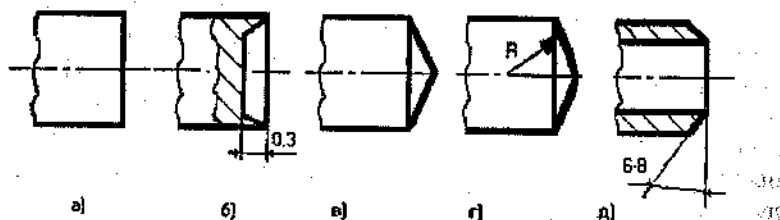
Форма торцов деталей для сварки сопротивлением: а) плоская поверхность (требует точной подготовки); б) кольцевой выступ (обеспечивает локальное тепловыделение и ограничивает поступление воздуха к стыку); в)–д) конус или сфера (локализует нагрев)
